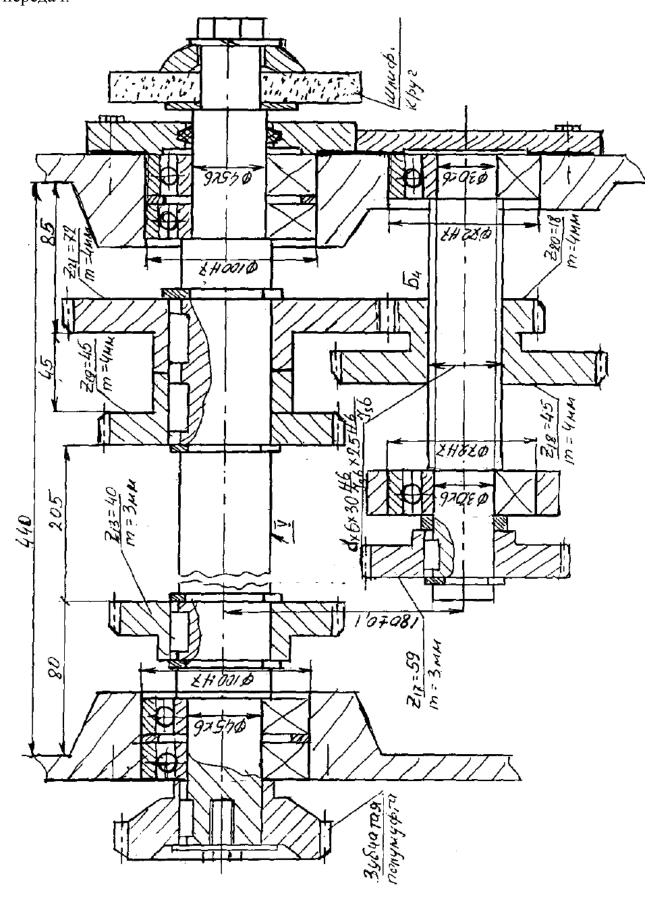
Сборочный чертеж наиболее нагруженной группы передач
